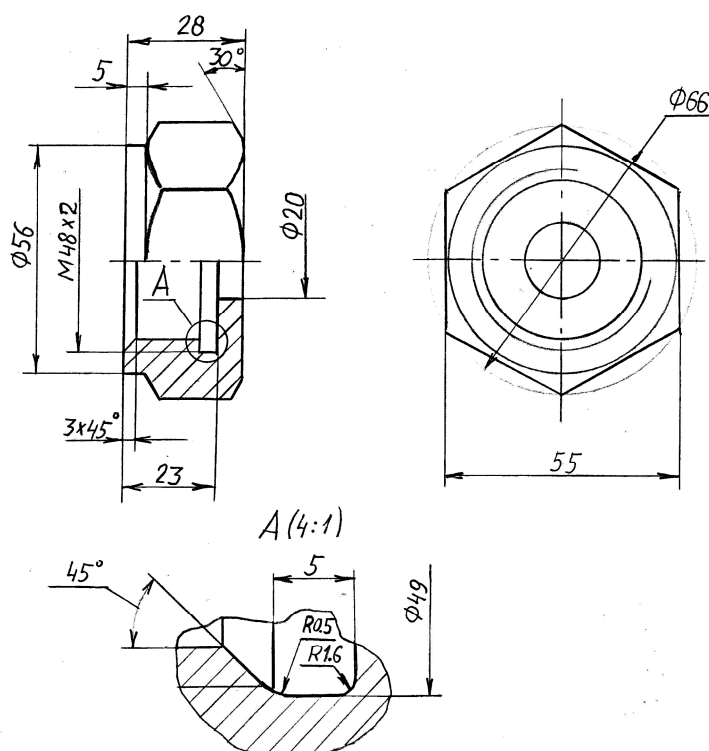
Изображения чертежа детали № 4 (Крышка)
